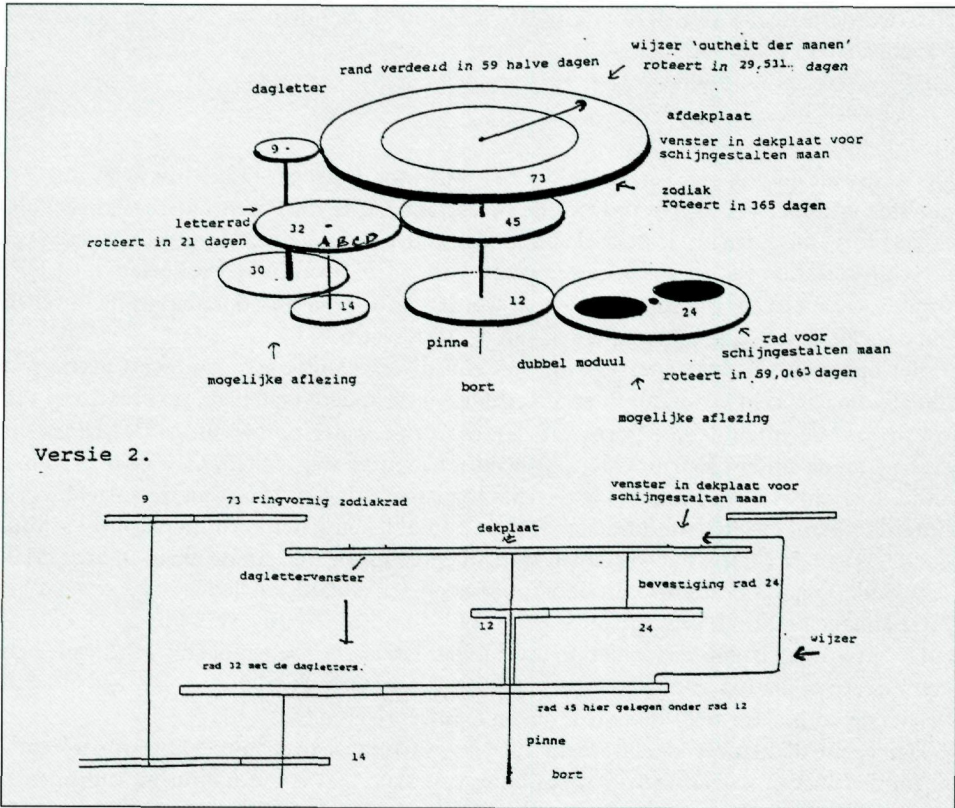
Constructieschetsen voor systeem 2 met een globale weergave van de ligging van de raderen.
